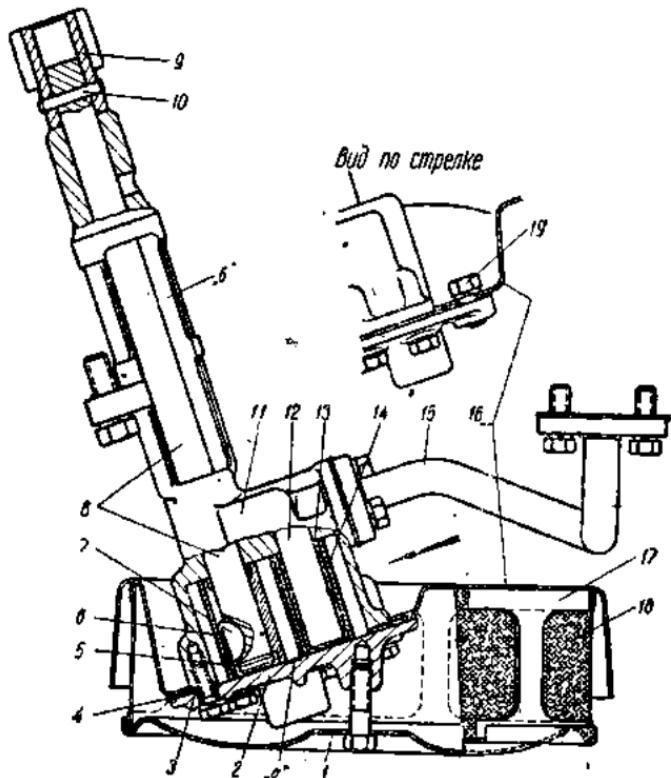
Масляный насос (1 — крышка маслоприемника; 2 — крышка корпуса насоса; 6 — ведущая шестерня насоса; 8 — вал привода насоса; 9 — ведущая шестерня вала насоса; 11 — корпус; 12 — ось ведомой шестерни; 14 — ведомая шестерня насоса; 15 — маслопровод; 16 — маслоотражатель; 18 — сетчатый фильтр).
